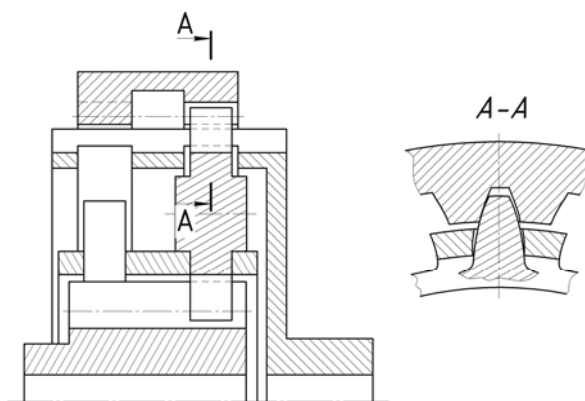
Коаксиальная безводильная планетарная передача типа ЗК с двухрядным расположением сателлитов
